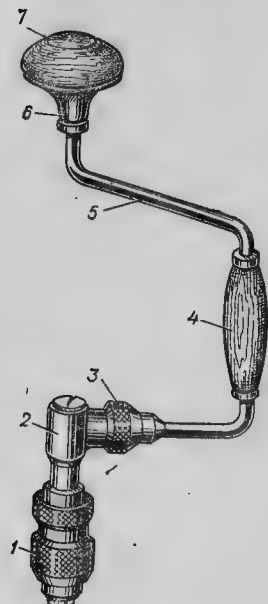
1 — патрон с зажимными кулачками; 2 — механизм сцепления; 3 — кольцо переключателя (реверс); 4 — ручка; 5 — стержень коленчатый; 6 — головка нажимная; 7 — ручка головки нажимной
